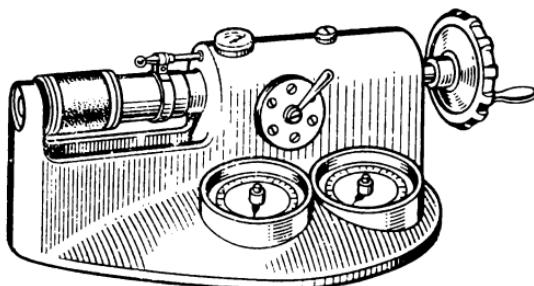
Универсальный прибор для определения прочности образцов из формовочных смесей
